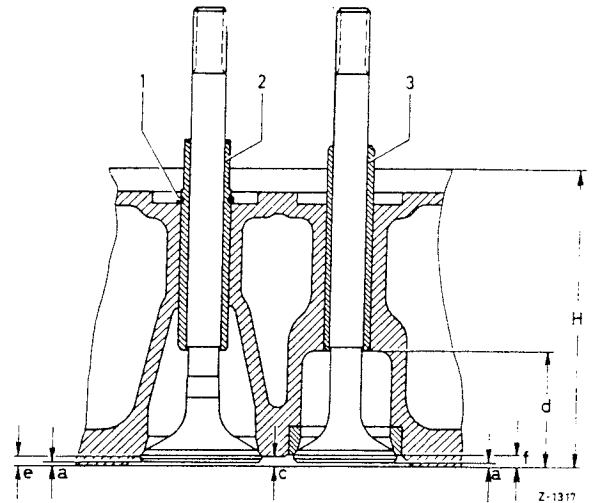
Zum Ab- und Planfräsen des Zylinderkopfes (OM 621)
